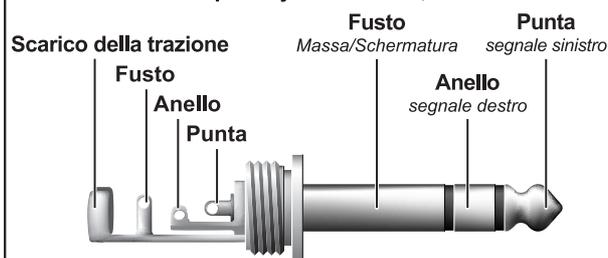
Cablaggio di una spina jack per cuffie stereo
